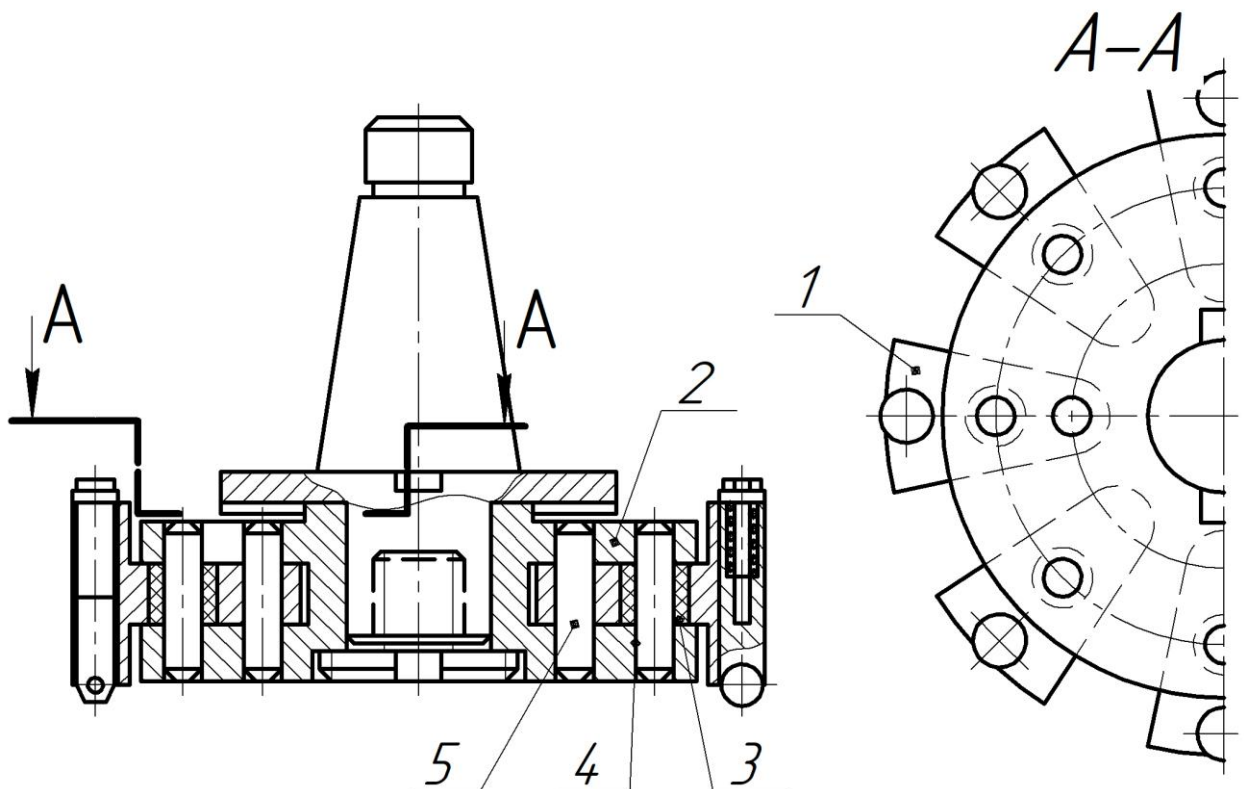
Конструкція фрези з шарнірними державками для під регулювання
